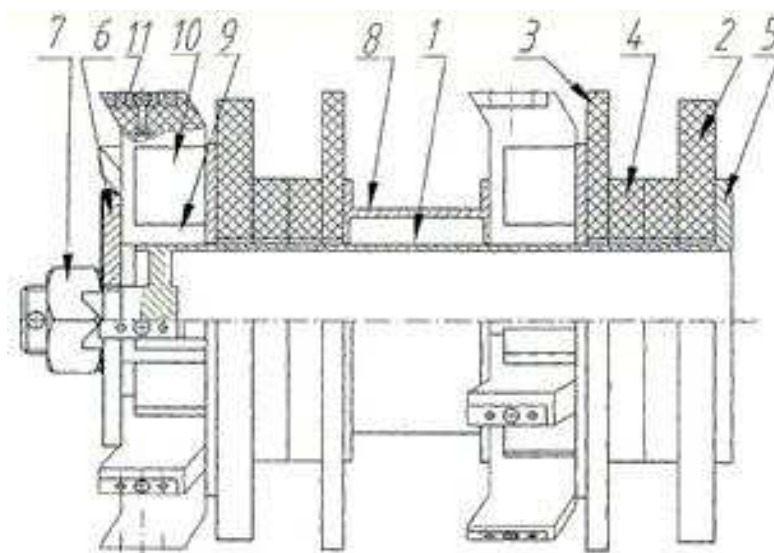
Скребок: 1 – корпус; 2.3.4 – блок дисков; 5 – фланец; 6 – поджимное кольцо; 7 – крепежный элемент; 8 – проставка; 9 – чистящий элемент; 10 – клык; 11 – зуб
